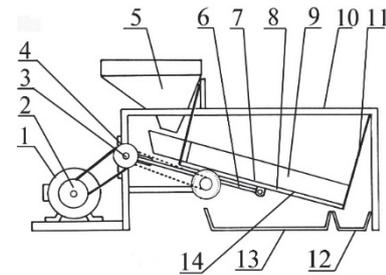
Конструктивная схема экспериментального плоскорешетного вибрационного сепаратора: 1 – электродвигатель; 2 – вариатор; 3 – вал; 4 – шайба эксцентриковая; 5 – бункер; 6 – шатун; 7 – стан решетчатый; 8 – очиститель шариковый; 9 – стенка прозрачная боковая; 10 – рама; 11 – подвески; 12, 13 – лотки; 14 – решето
